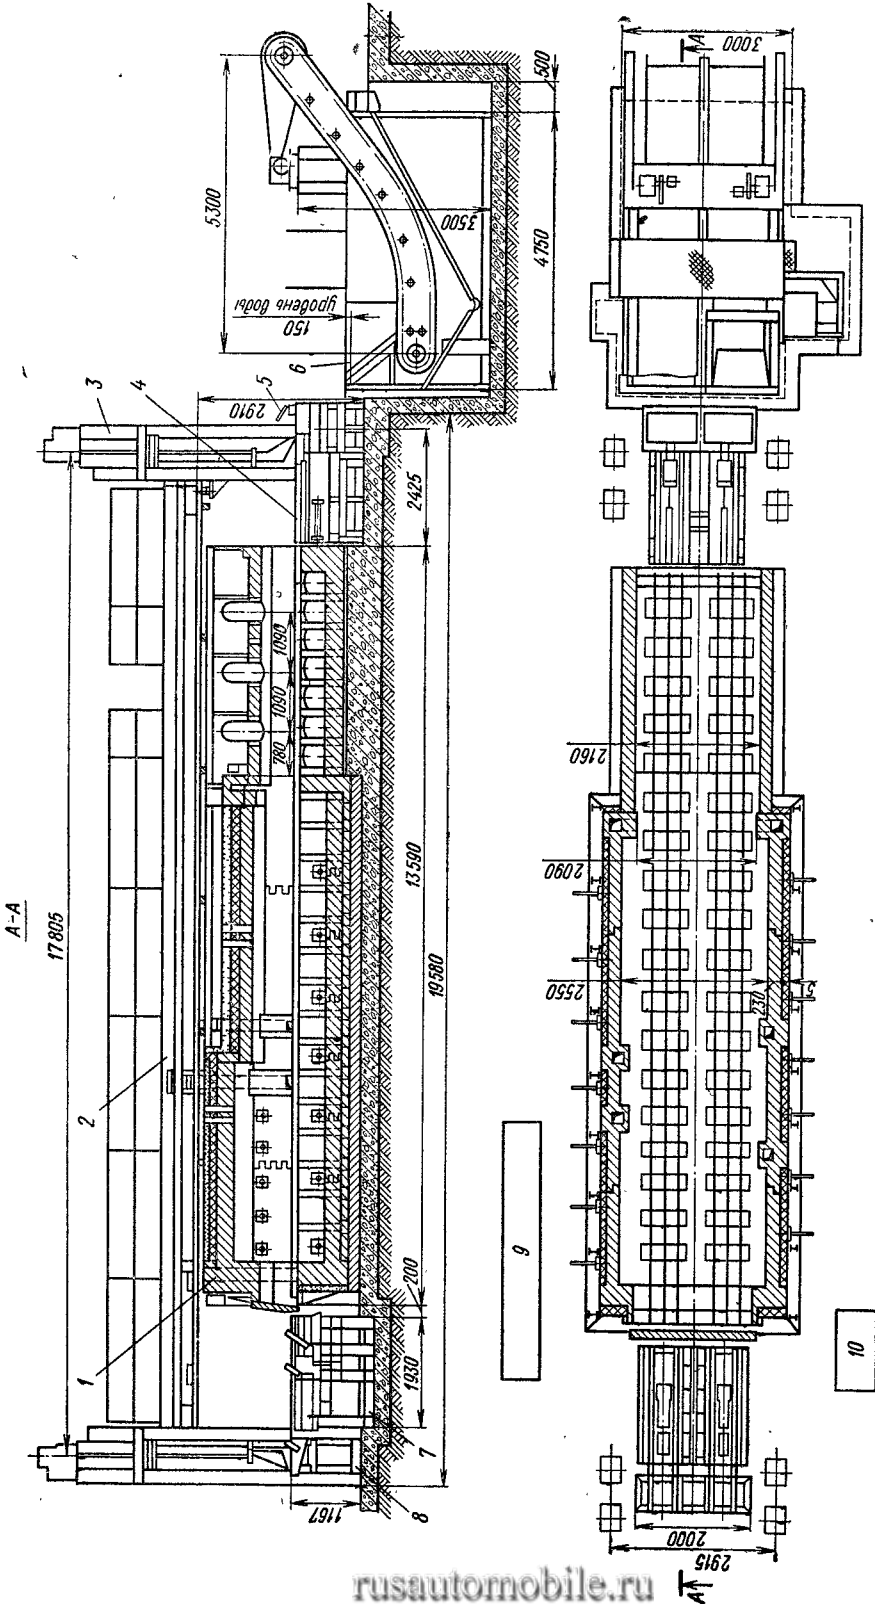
Автоматизированный агрегат для нормализации отливок:
